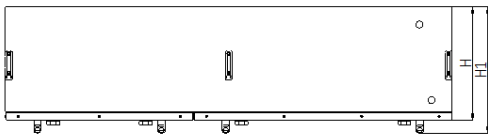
Компактная установка EVO-T+ 5000; EVO-T+3000 (вид снизу для подвесной версии / вид сверху для лежащей версии).
